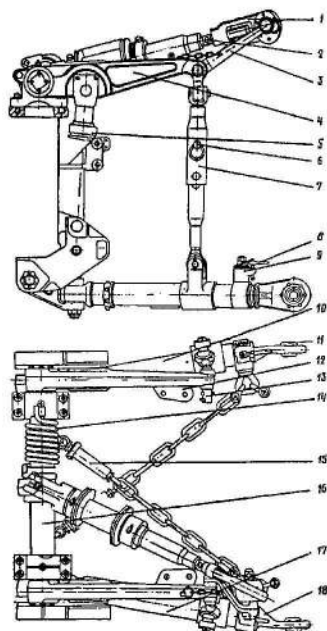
Навесное устройство: 1 - центральная тяга; 2 - стяжной винт; 3 - кронштейн; 4 - главный рычаг; 5 - гидроцилиндр; 6 - палец; 7 - вертикальный раскос; 8 - рукоятка; 9 - замок; 10, 17 - нижние тяги; 11 - шарнир; 12 - площадка; 13 - насадка; 14 - уравновешивающая пружина; 15 - горизонтальный раскос; 16 - вал; 18 - выдвижные тяги.
